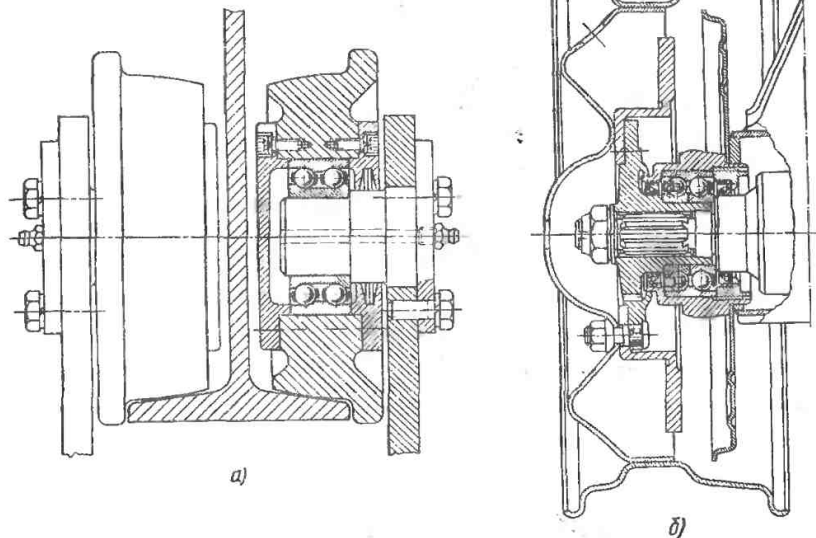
Установка опорных колес на одном двухрядном радиально-упорном шарико-подшипнике
